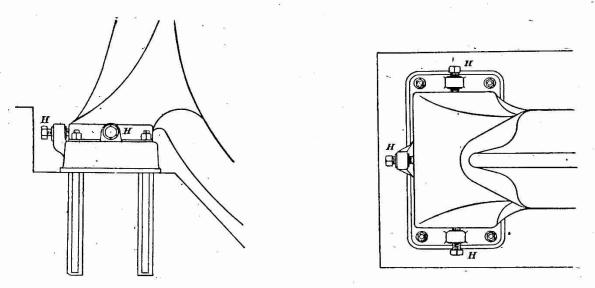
Montage de la carcasse de l'induit sur la plaque de fondation. H, vis permettant de déplacer la carcasse dans un plan horizontal.
